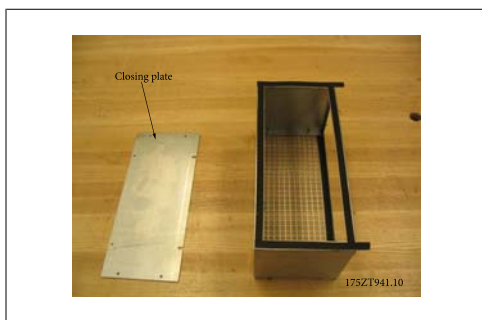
Собранный верхний воздуховод с прокладкой
